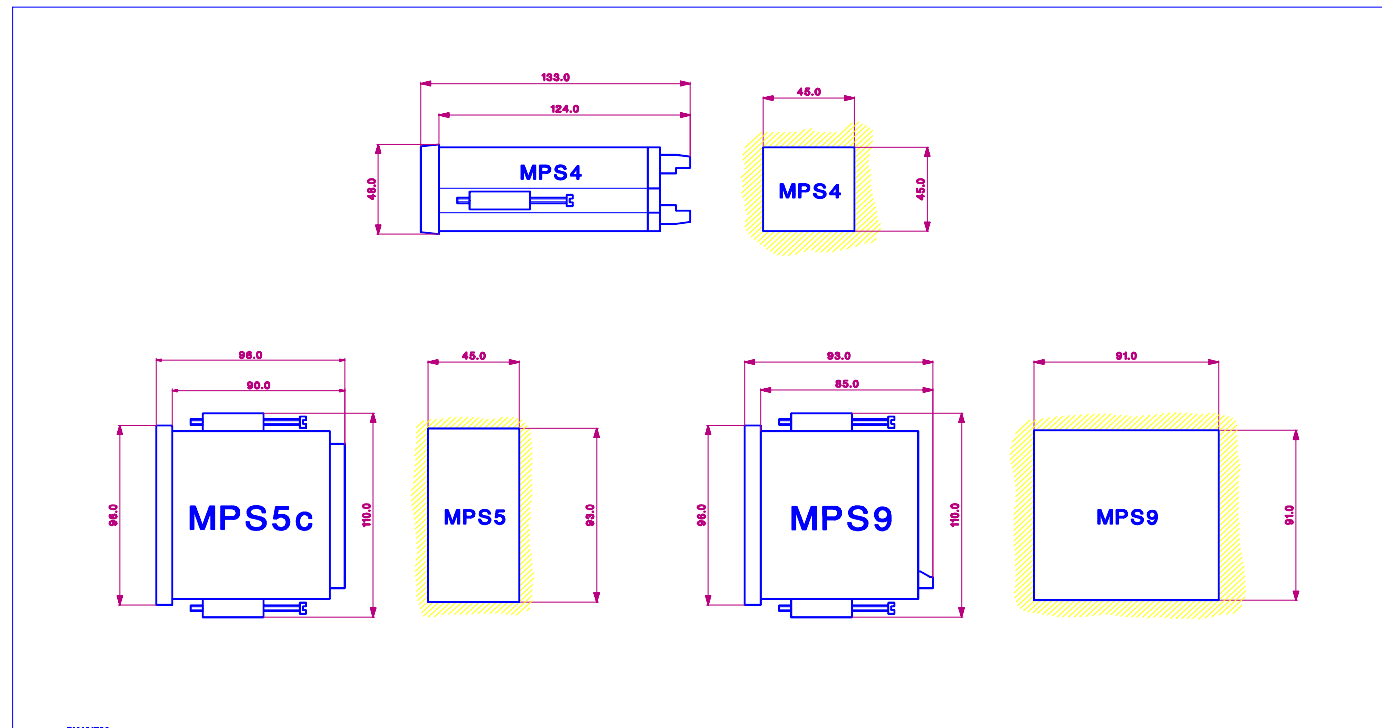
DIMENSIONI E FORATURA PANNELLO - DIMENSIONS AND PANEL CUTOUT
